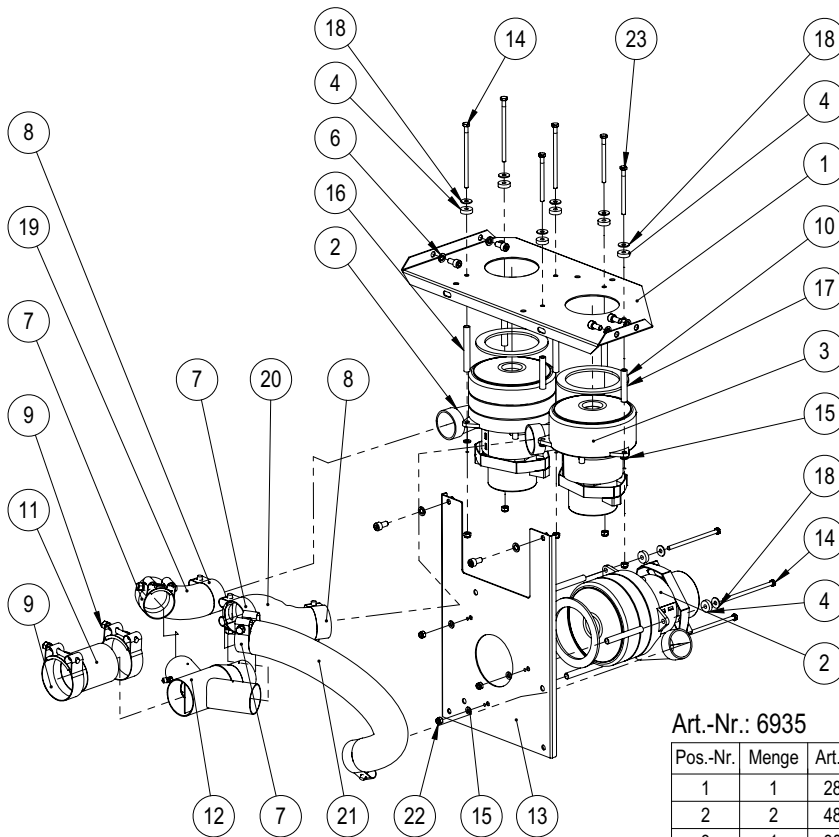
Explosionszeichnung Maschinenaufbau M95 400V 7,0kW
